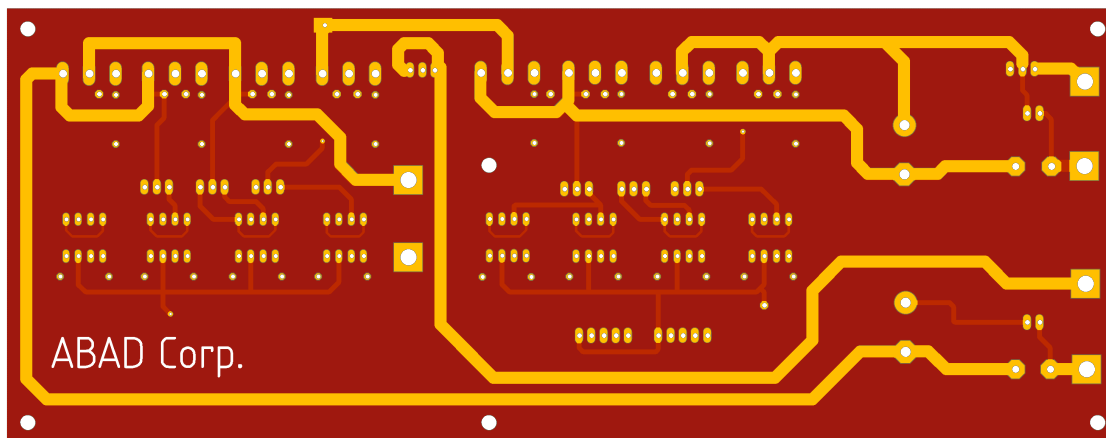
Vista previa del PCB en la capa inferior antes de fabricar.
